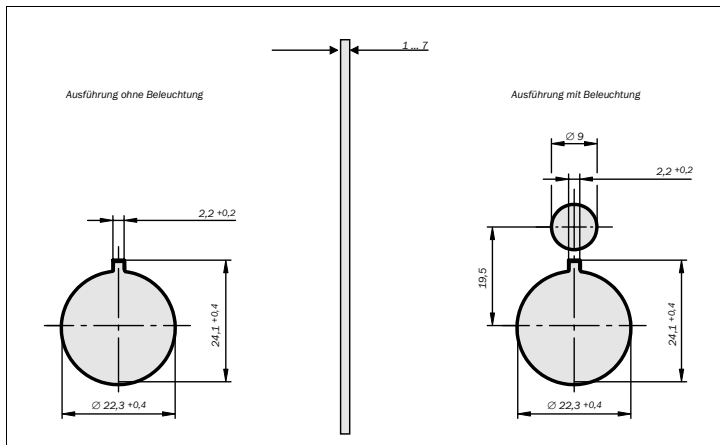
Maßbilder der Montagelöcher für die Einbauversionen (mm)
